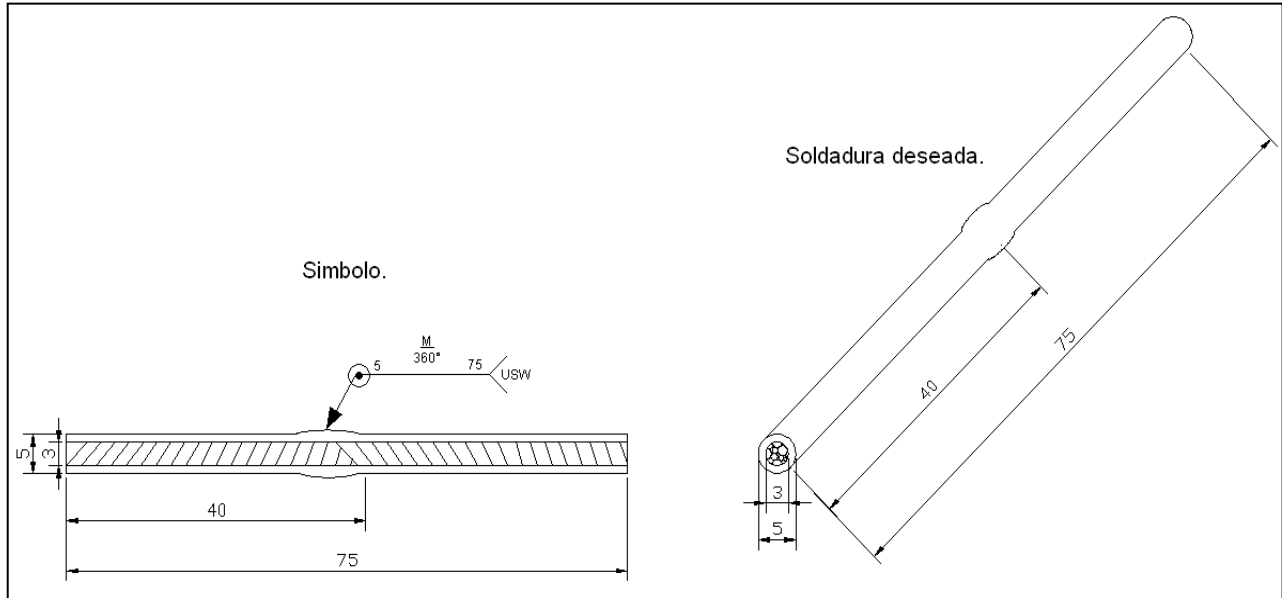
Ejemplo de cable soldado por el método de Soldadura Ultrasónica (USW). Diagrama de soldadura y símbolo de esta.
